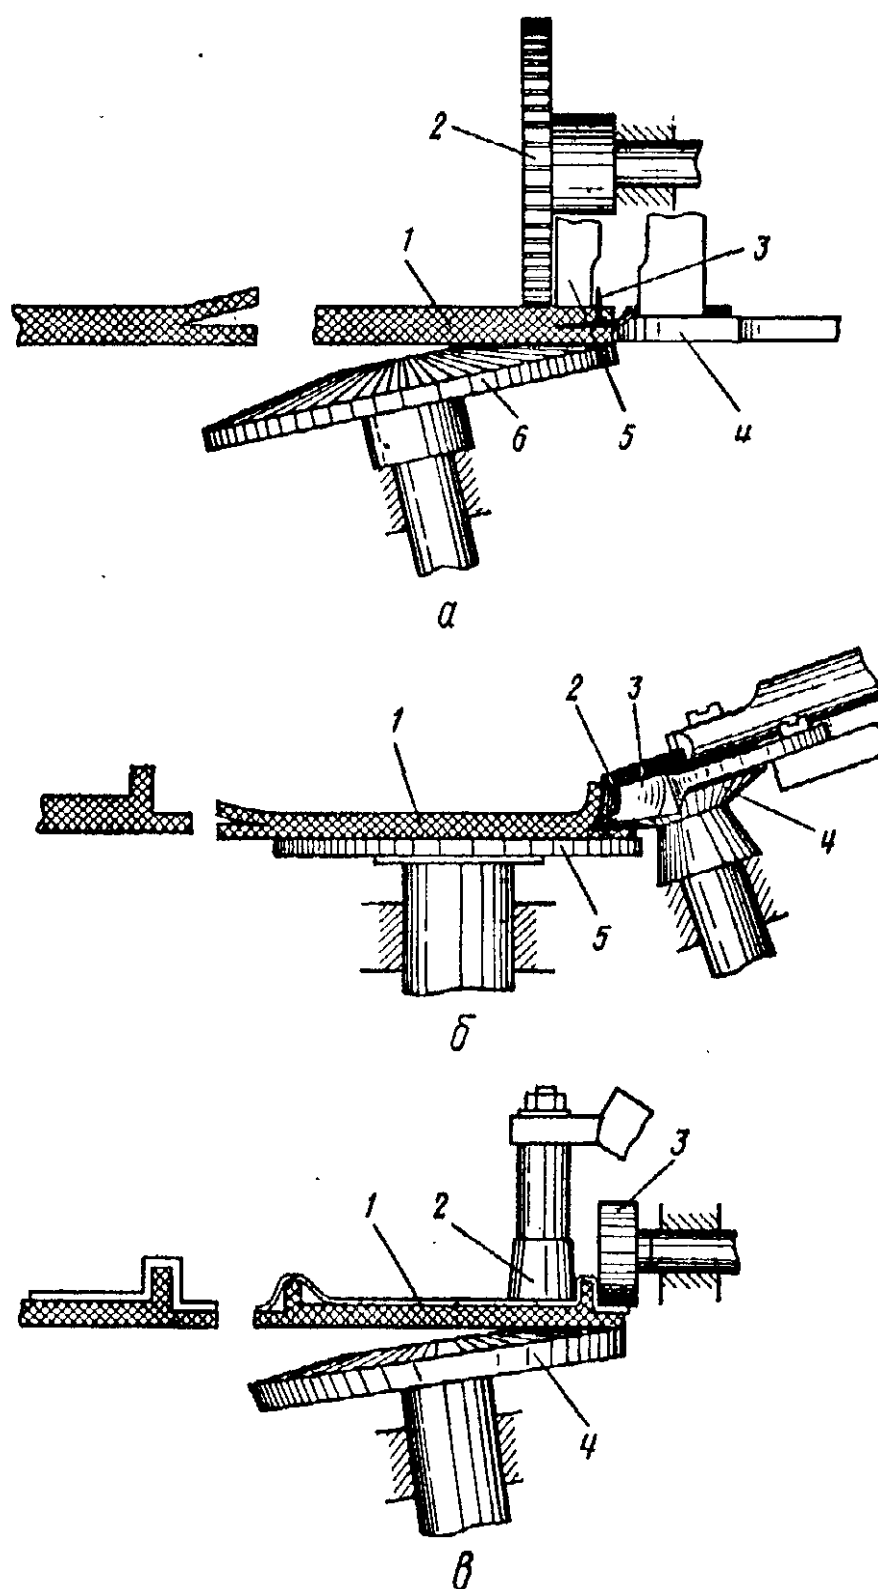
Схемы последовательности обработки рантовой стельки на машинах: а — 05022/Р1; б — 05134/Р3; в — 05038/Р3
